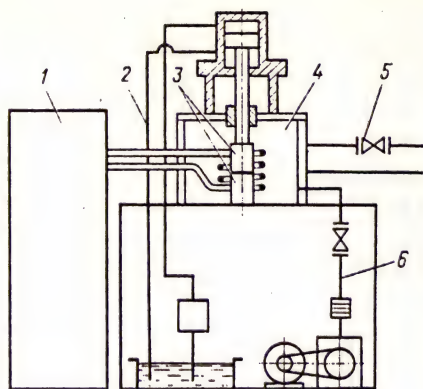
Схема установки для диффузионной сварки:
